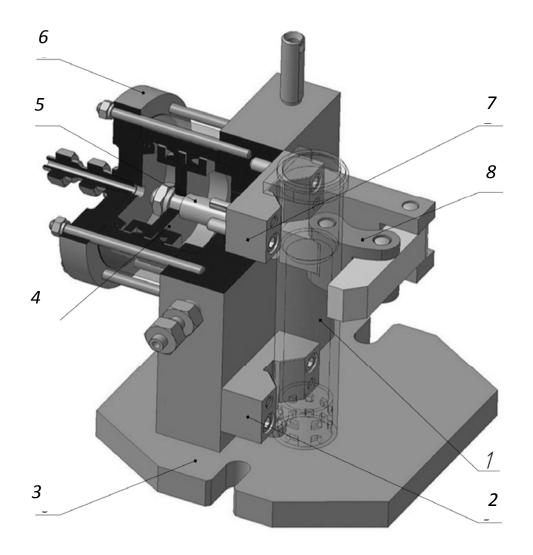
Сборочный чертеж и 3D-модель приспособления для механической обработки детали «Муфта» на вертикальнофрезерном станке с ЧПУ Mazak INTEGREX 100-IIIST: 1 – заготовка; 2, 7 – призмы; 8 – серьга; 6 – цилиндр; 4 – поршень; 5 – шток; 3 –основание
